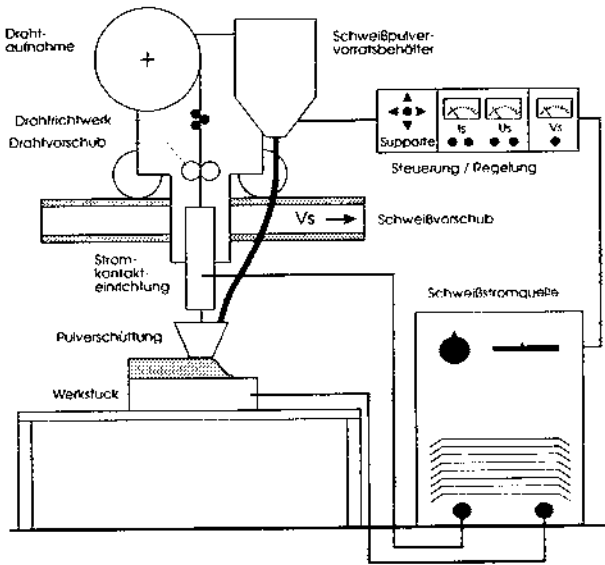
Verfahrensprinzip des Unterpulverschweißens.
